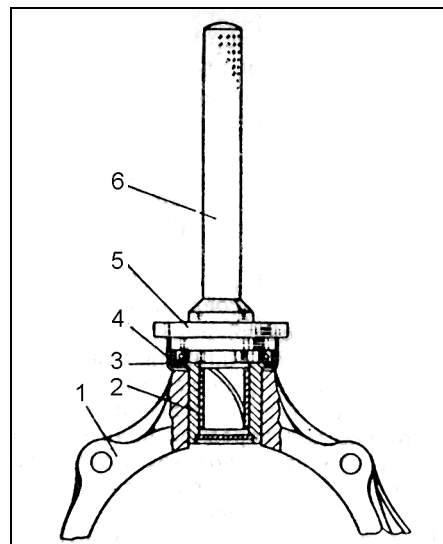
Запрессовка сальника шкворня: 1 – кулак поворотный; 2 – корпус втулки шкворня с втулкой в сборе; 3 – обойма сальника; 4 – сальник; 5 – оправка (рис. 156); 6 – ручка (рис. 157).
